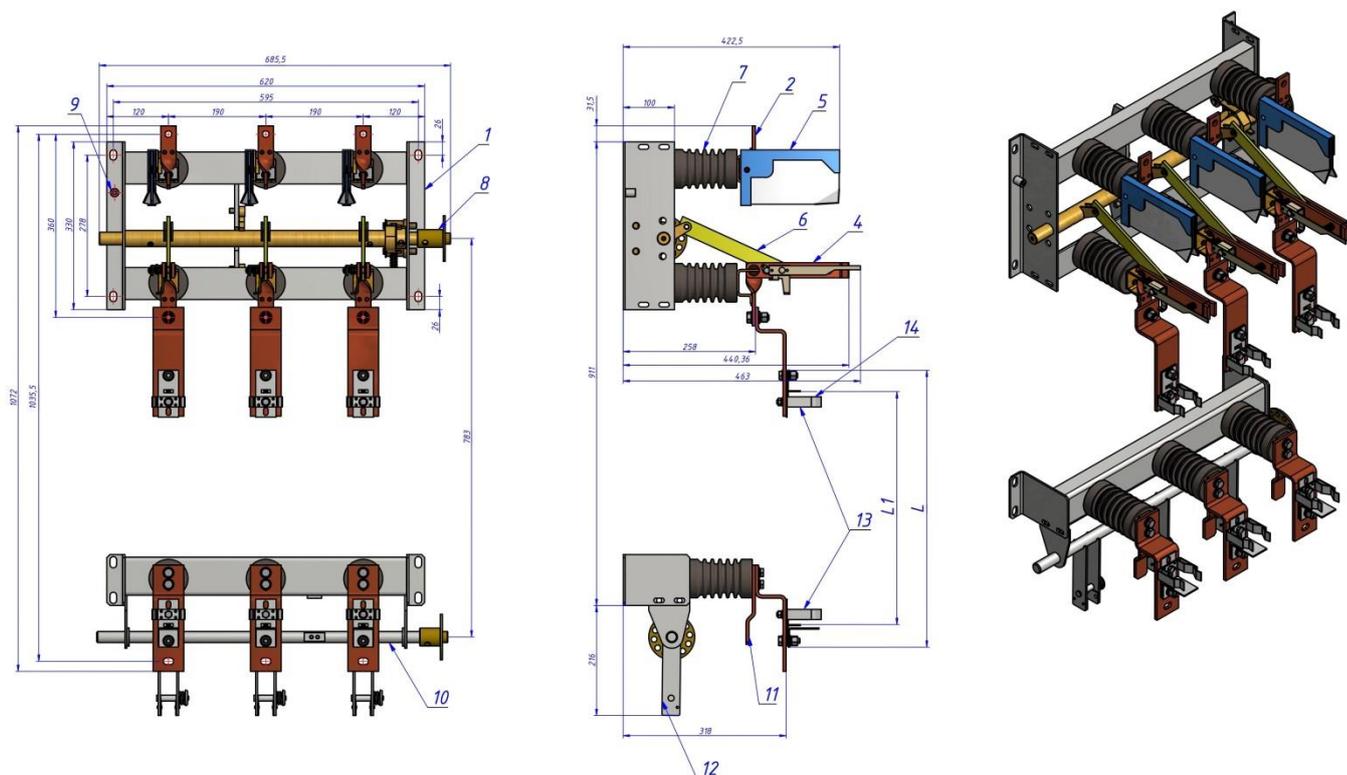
Габаритно-установочные размеры и устройство ВНА (с открытыми ножами и под ножи заземления)
